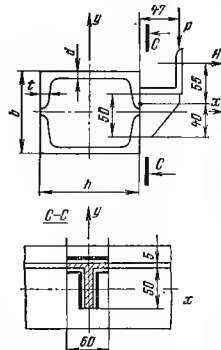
Схема к расчету опорного угольника крошштейна.
